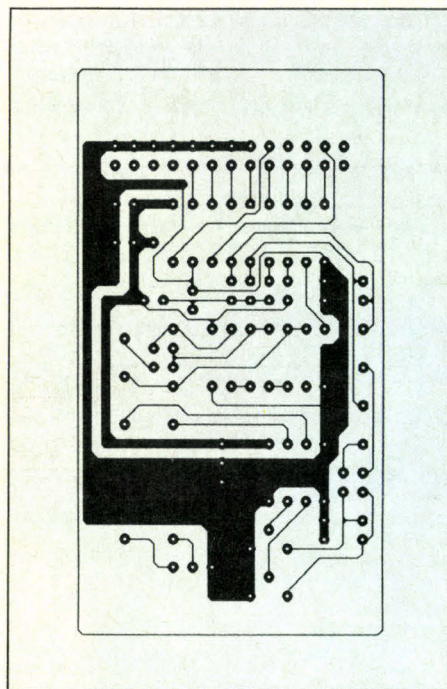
Circuit imprimé vu côté soudure.
